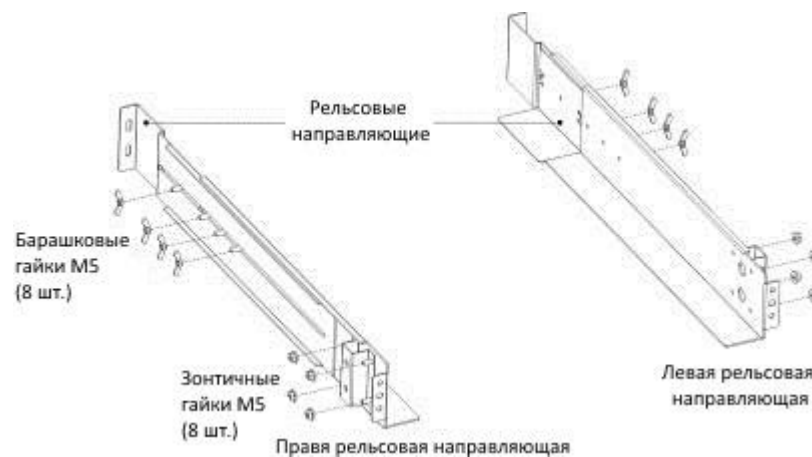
Установка и регулировка рельсовых направляющих
